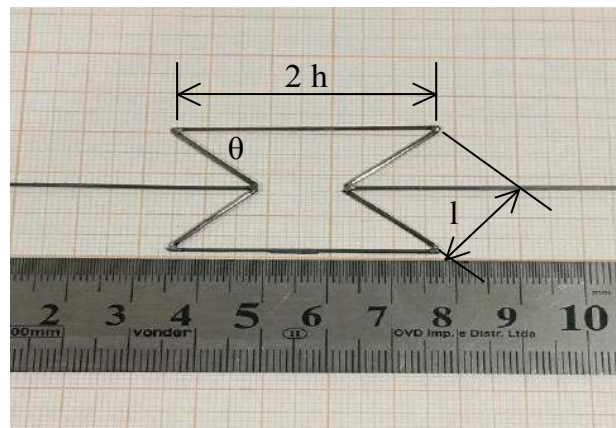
Célula de LMF Ni-Ti fabricada por meio de micro-soldagem autógena TIG.
